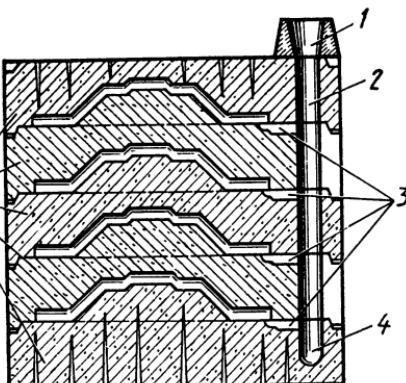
Схема конструкции ярусной литниковой системы для отливки крупной стальной детали (шайба):
